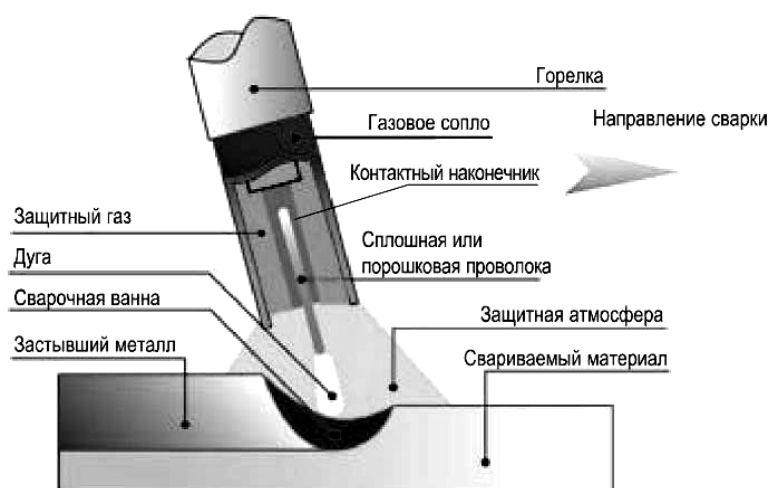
Схема процесса сварки в защитных газах плавящимся электродом
